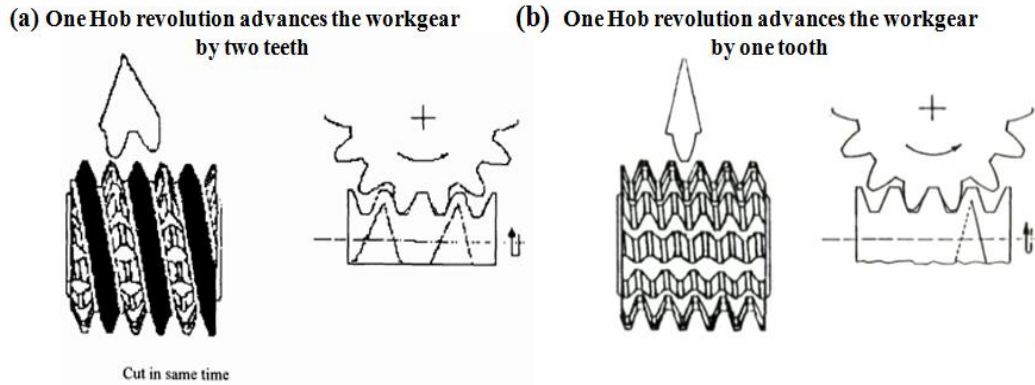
Illustration 3D d'un outil fraise-mère (a) à deux filets (b) à un seul filet, [8].
